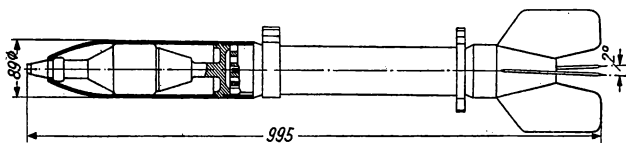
Flugzeug-Panzerrakete mit Hohlladung
